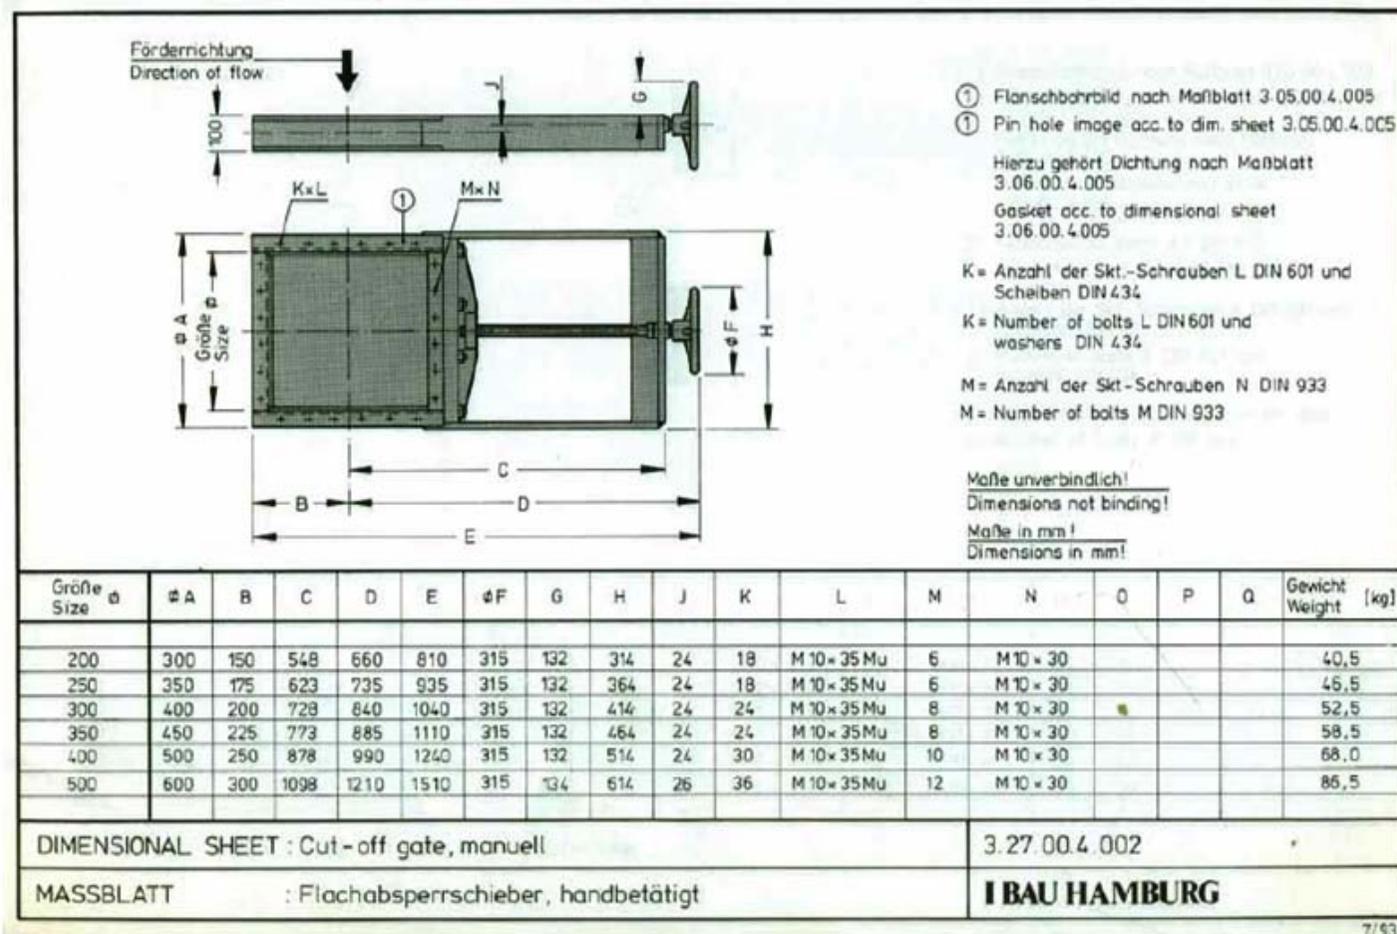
DIMENSIONES DE VÁLVULA GUILLOTINA [7]
